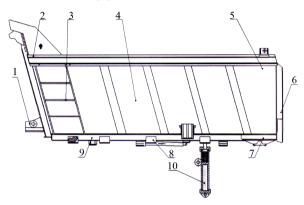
Безопасное опрокидывающее устройство кузова СТС с гидравлическим приводом: I — передний упор; 2 — рама; 3 — лестница; 4 — борт; 5 — поперечина; 6 — задний борт; 7 — опора подвижная; 8 — опора резиновая; 9 — днище; 10 — упор предохранительный
